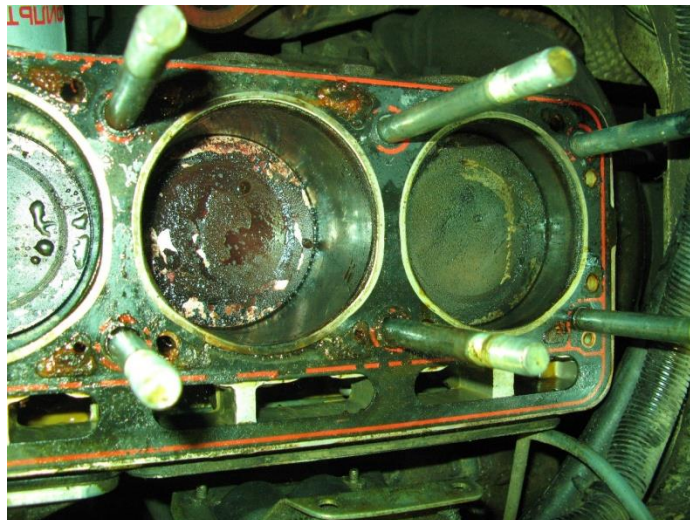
Нагар на днищах поршней двигателя автомобиля ГАЗ-172452
